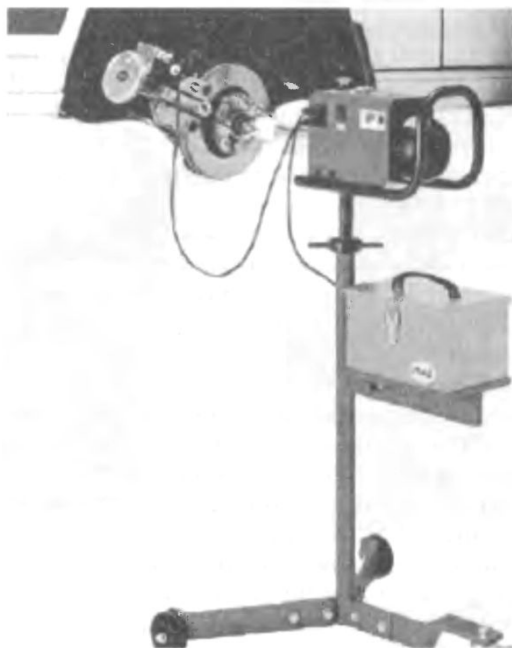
Станок для двусторонней проточки тормозных дисков легковых автомобилей DL 87001 фирмы MAD-TOOLING (Нидерланды)
